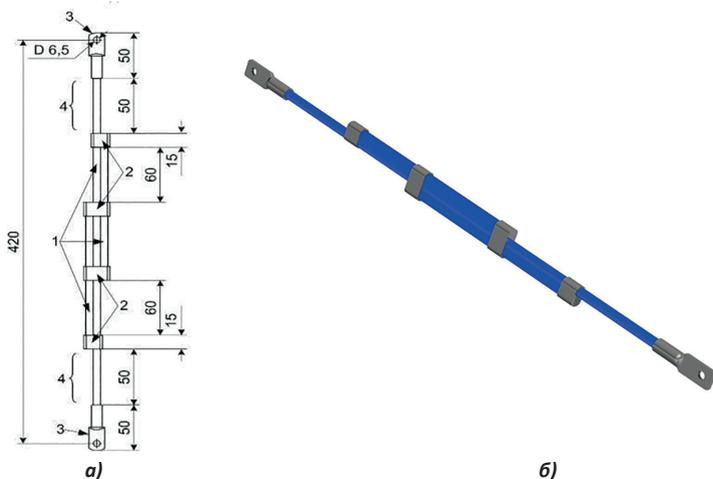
Внешний вид и конструкция РДИМ-10-К: а) габаритные размеры; б) внешний вид; 1–разрядные модули; 2–металлические втулки; 3–металлические оконцеватели; 4–искровые промежутки.
